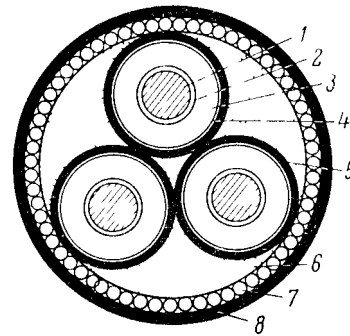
Трехжильный кабель с отдельно оцинкованными жилами для подводной прокладки.
